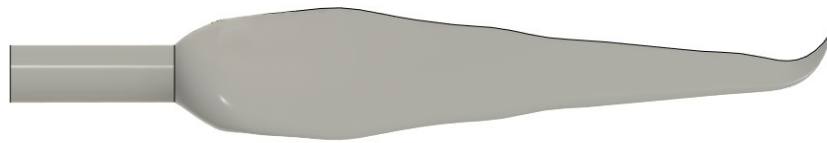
Vista de planta de la pala FPP Caso 2 - Modificado.
